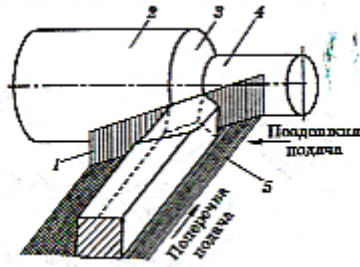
Поверхні оброблювальної заготовки і координатні площини.
